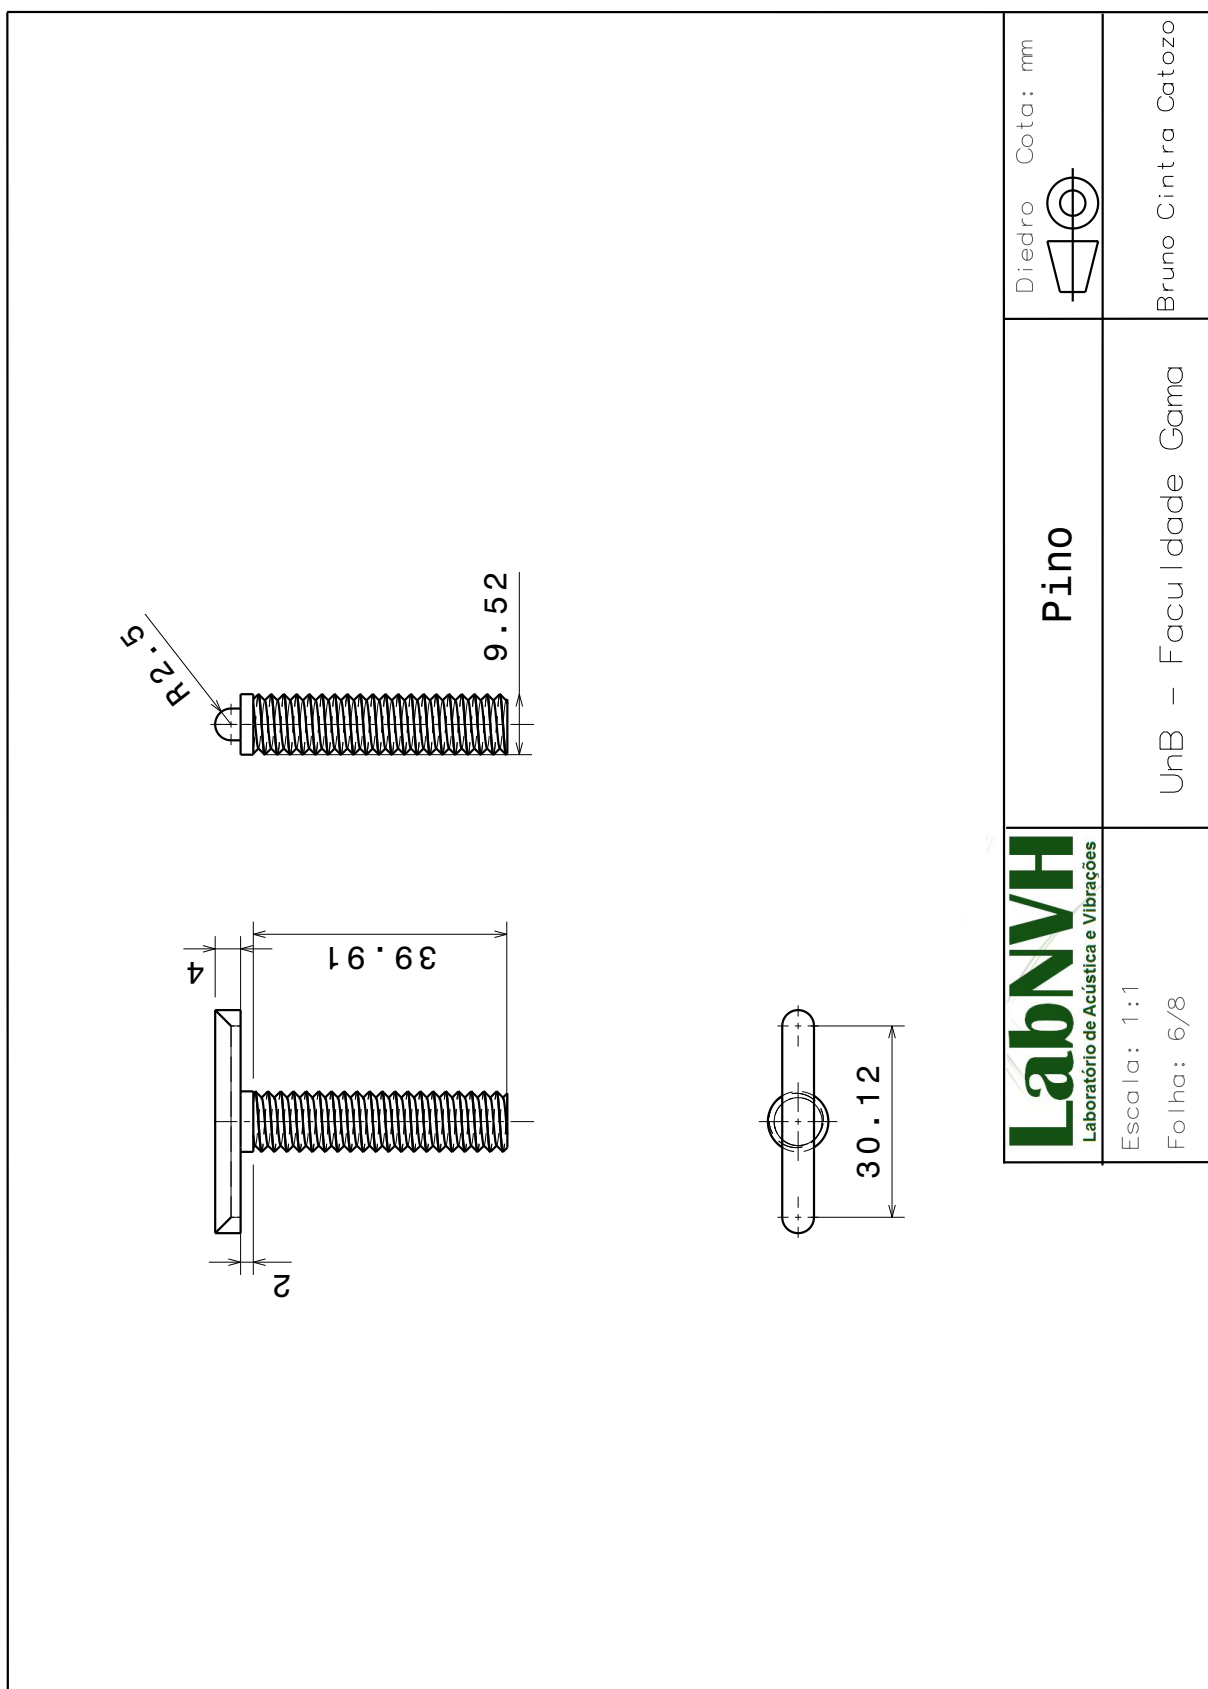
Desenho técnico do pino superior de aço SAE 1020
